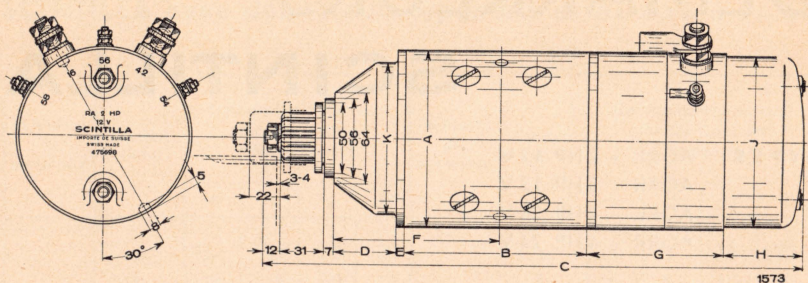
Dimensions d'encombrement pour démarreur type AGR
